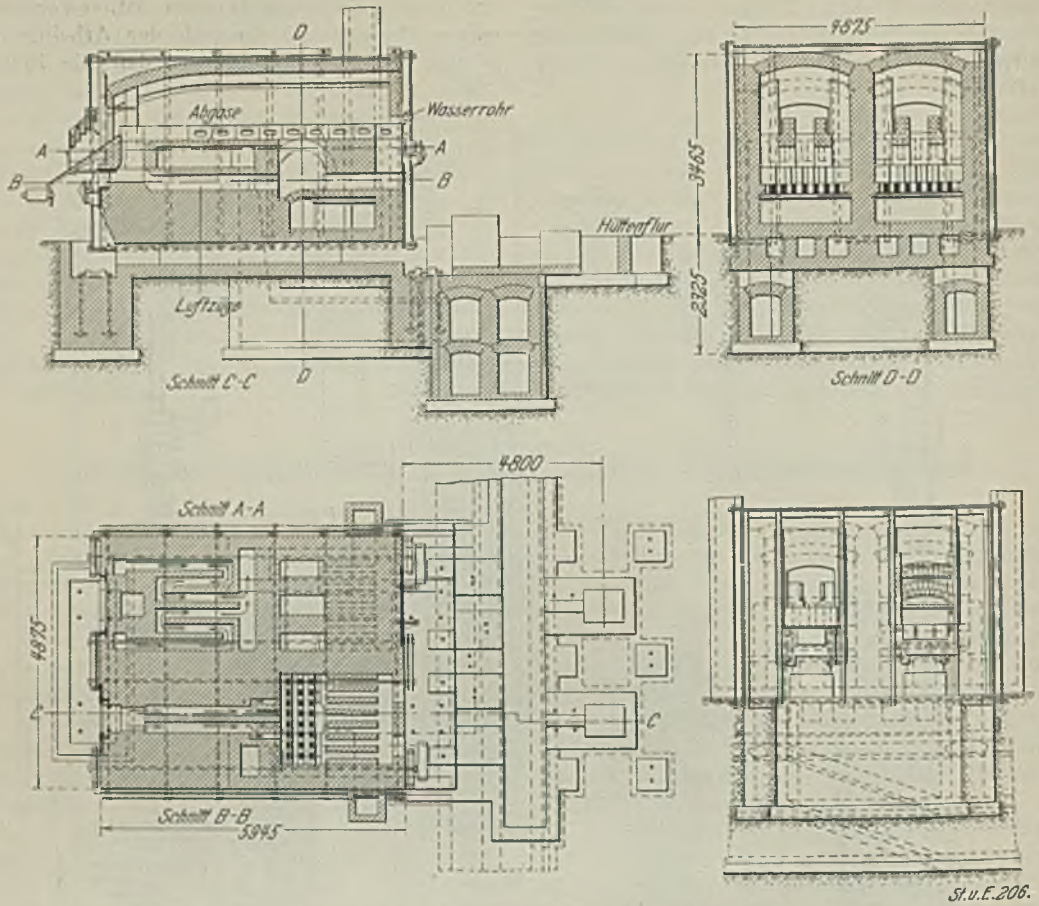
Grundriß und Schnitte des kontinuierlichen Wärmeofens.
